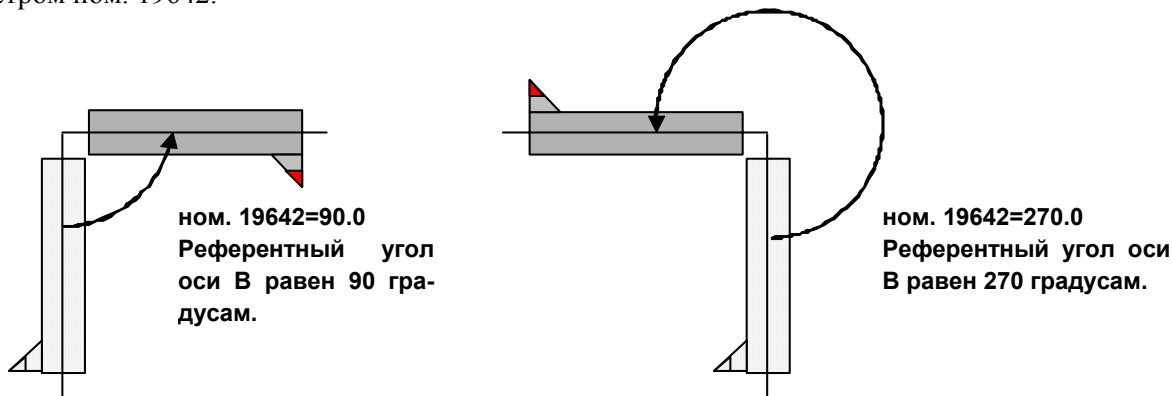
(c) Референтный угол оси поворотной головки (ось B)
